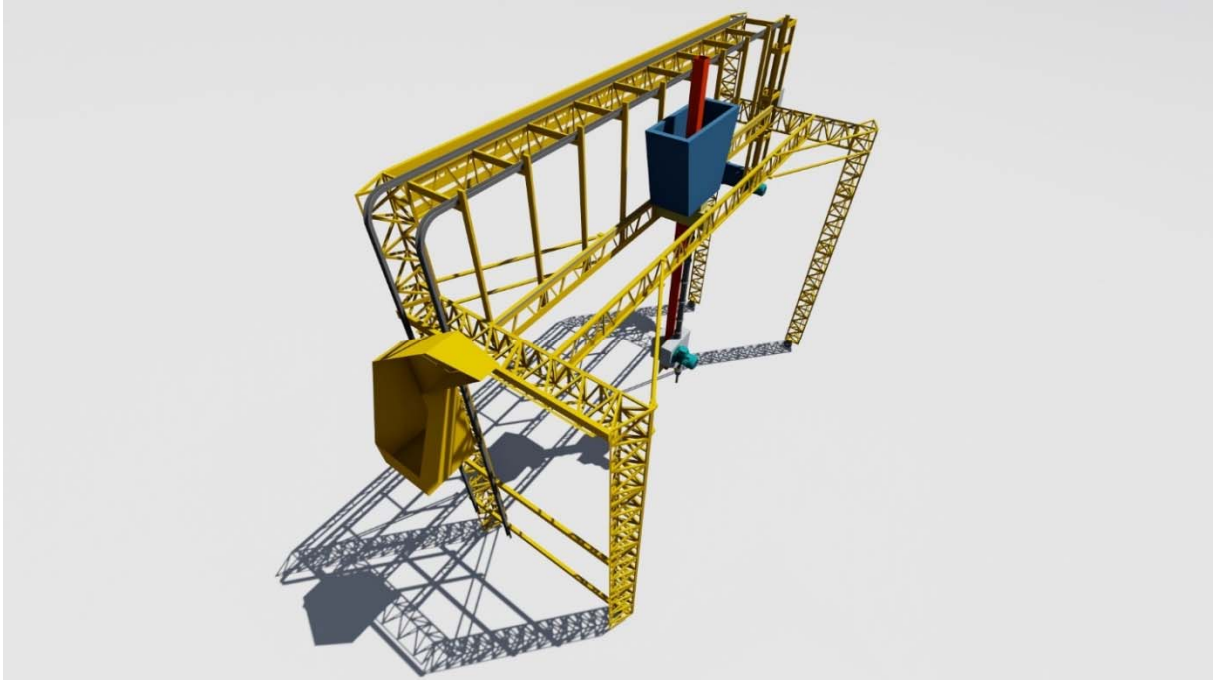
32. Impresora de coordenadas rectangulares con estructura aporricada. Vista lateral
